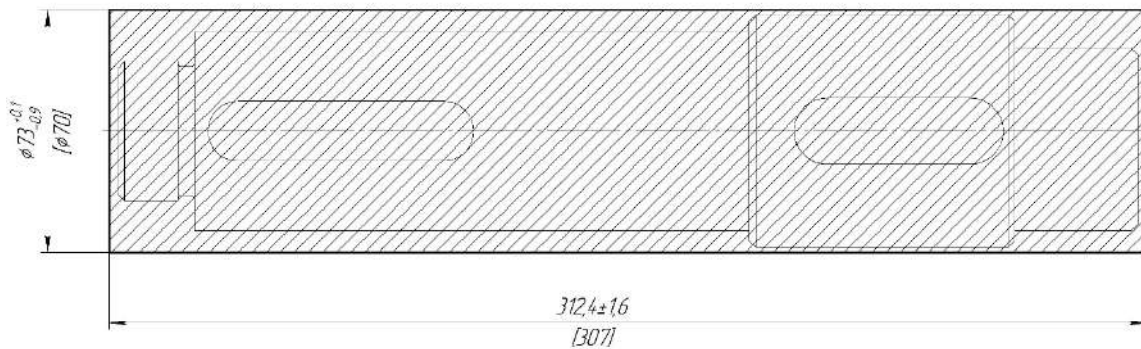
Ескіз заготовки, що отримана з прокату
